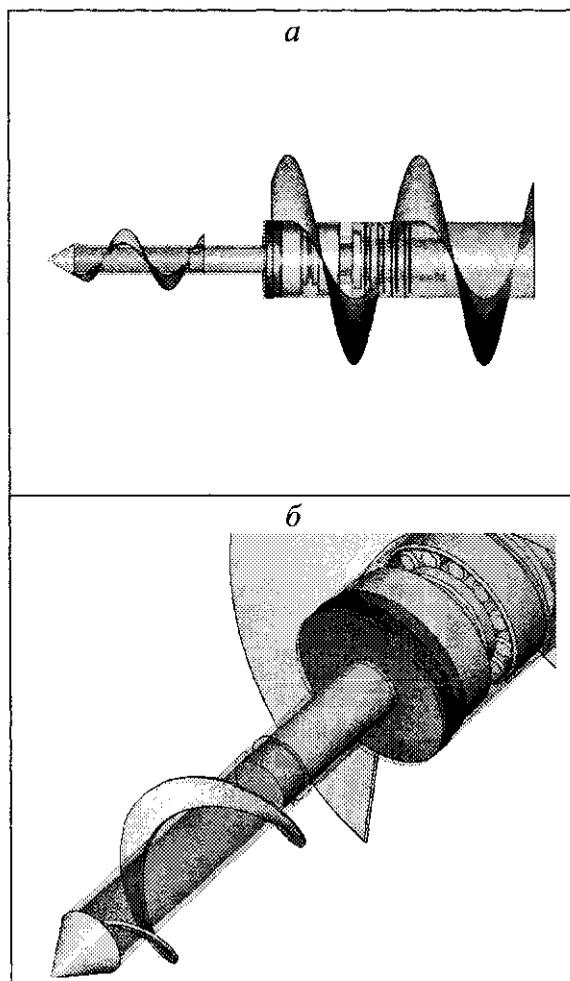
Расширитель прямого хода с анкер-забурником: общий вид (а); подшипниковый узел (б)
